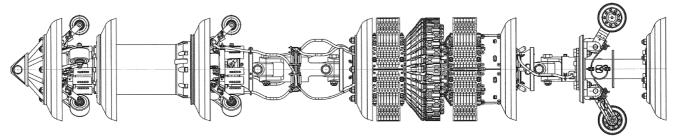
Чертеж общего вида дефектоскопа внутритрубного магнитного 12-MCK.01-00.000-01 и 14-MCK.01-00.000-01
